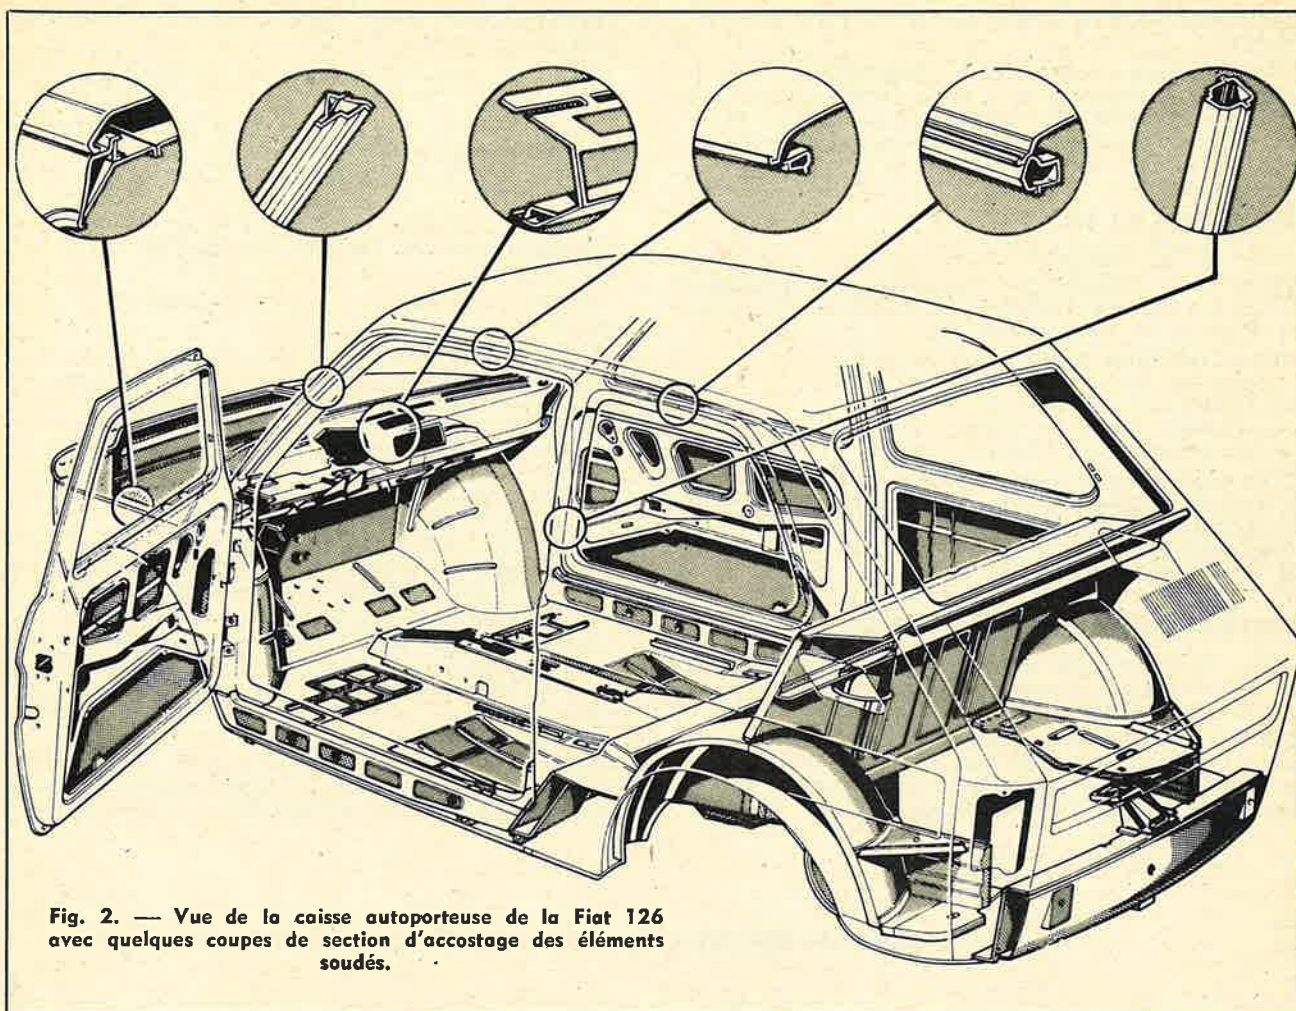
Vue de la caisse autoporteuse de la Fiat 126 avec quelques coupes de section d'accostage des éléments soudés.
